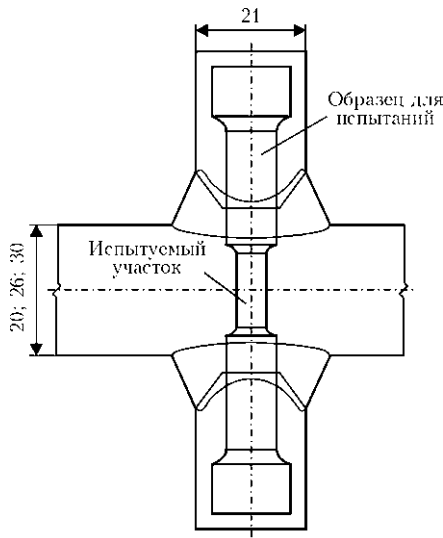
Схема вырезки образцов из сварных соединений, выполненных в соответствии с ГОСТ 28870-90
